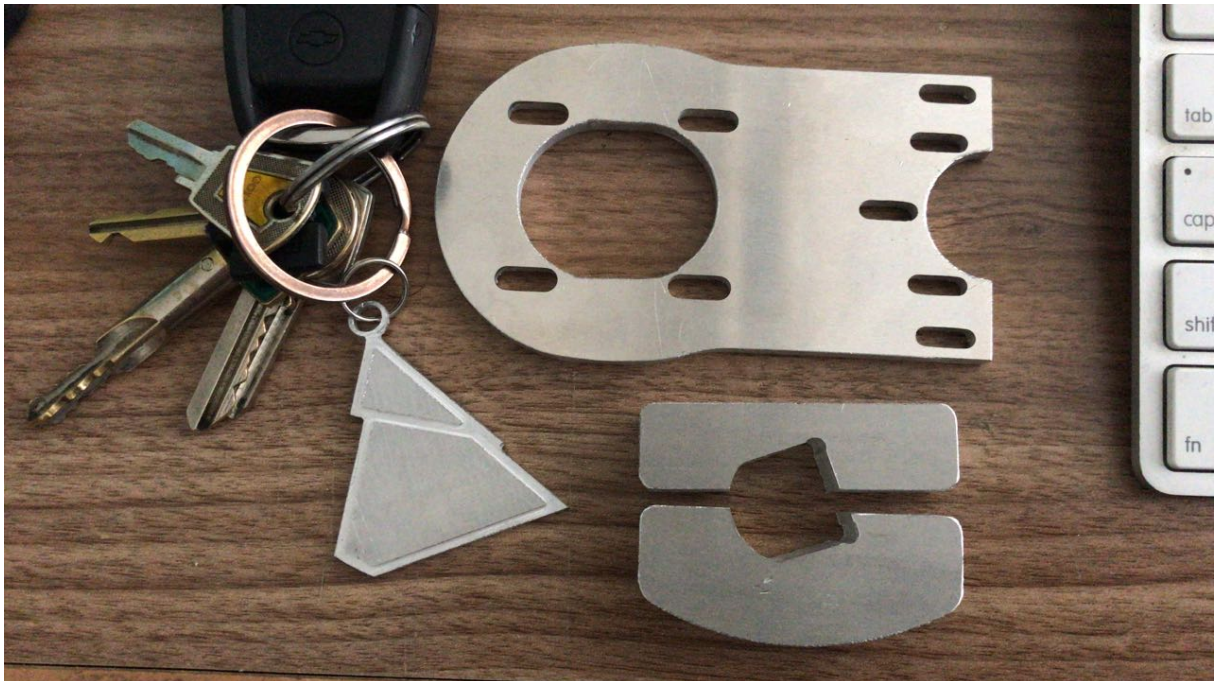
Peças do suporte do motor cortadas em alumínio
